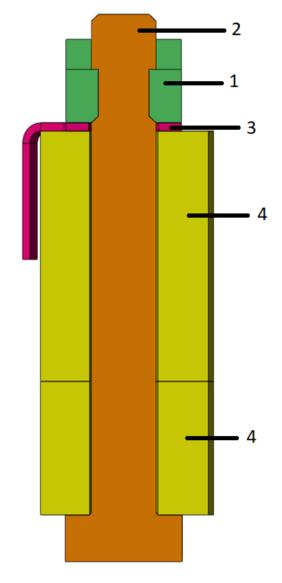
Вид с разрезом: 1- гайка, 2 — болт, 3 — шайба, 4 - пластины
